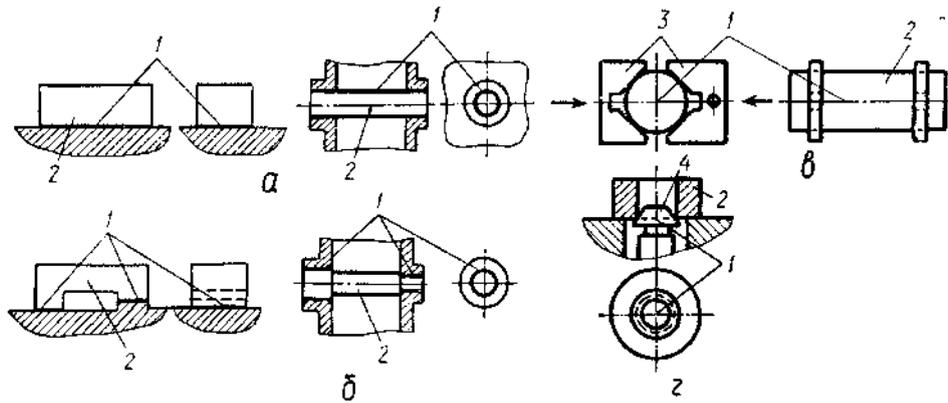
Приклади базування: 1 - база; 2 - заготовка; 3 - затискні губки; 4 - конус центрального пристрою
